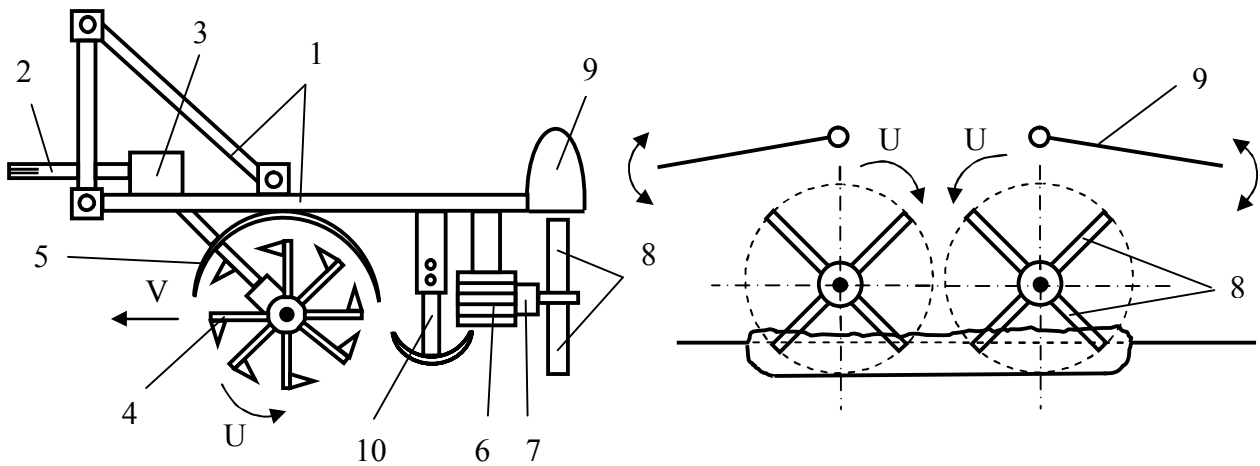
Грунтомет пожарный фрезерный СГАУ:
